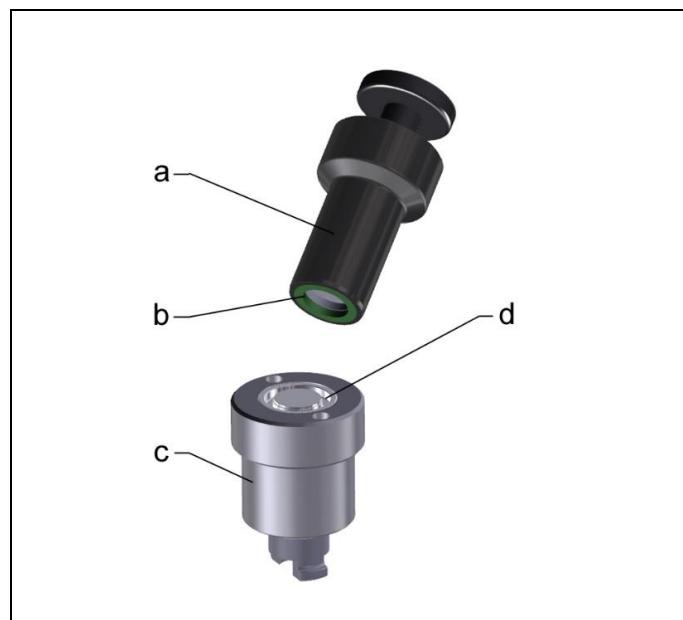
Herramienta de montaje equipada con arandela junta, antes del clavado en el mecanismo de conexión.
